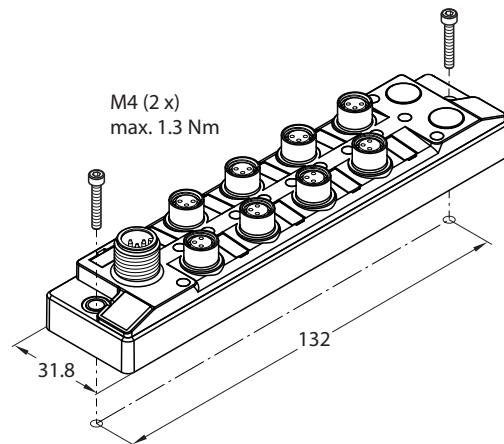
Gerät auf Montagefläche befestigen (Beispiel: MD 742-...)
